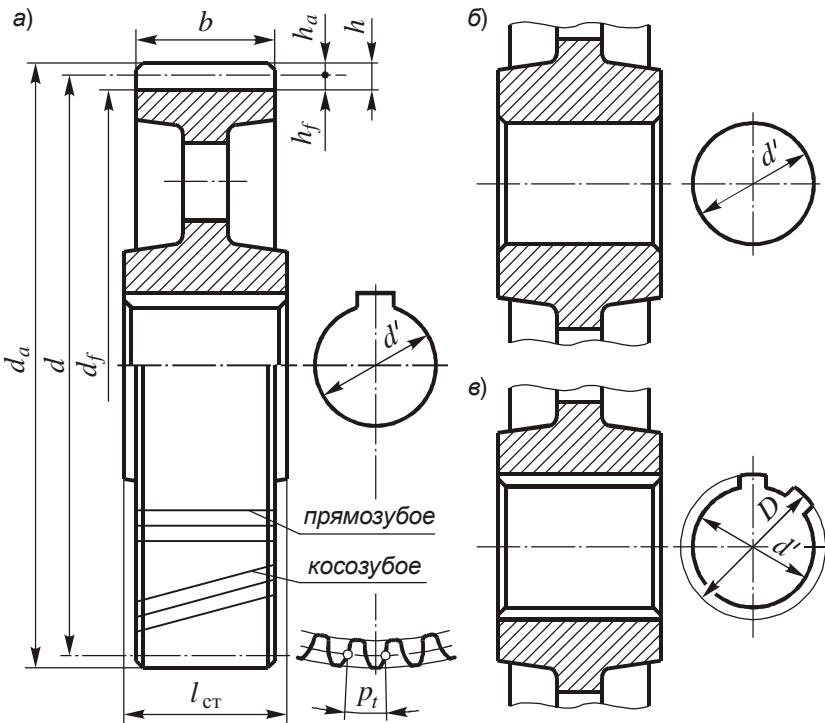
Эскиз зубчатого колеса: *а* – со шпоночным пазом; *б* – с гладким отверстием; *в* – с прямобочными шлицами
